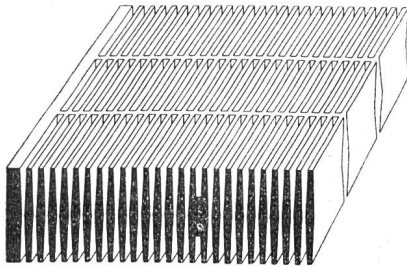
Positive Platte, Querschnitt. — Plaque positive en coupe.
